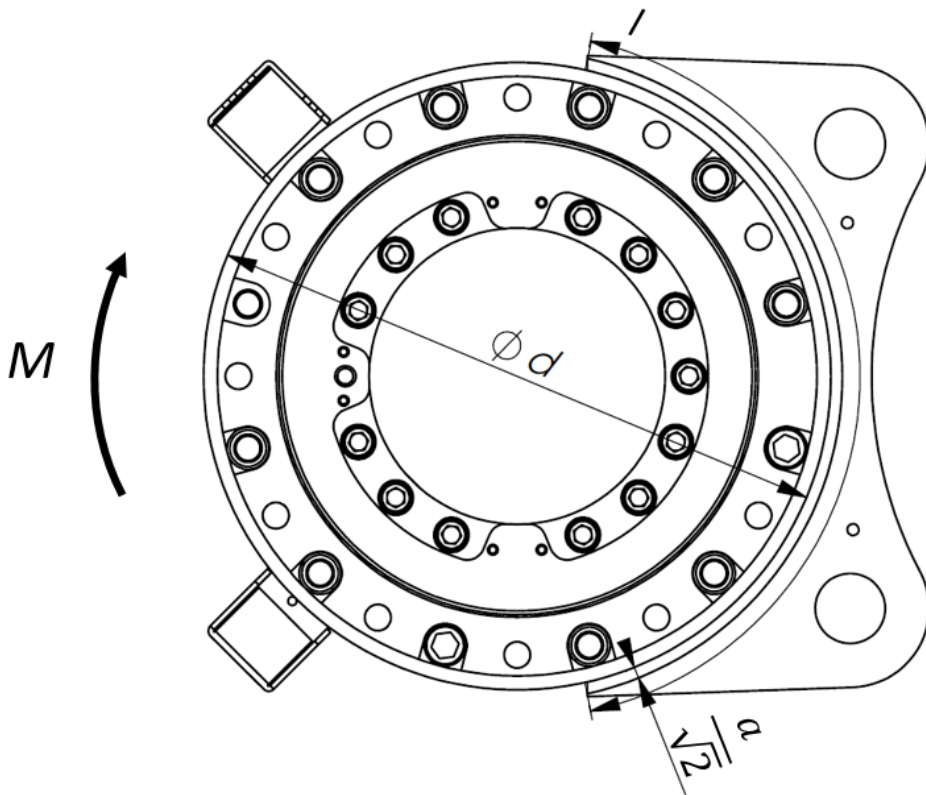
Maße Schweißnaht, Quelle: Schwing GmbH
